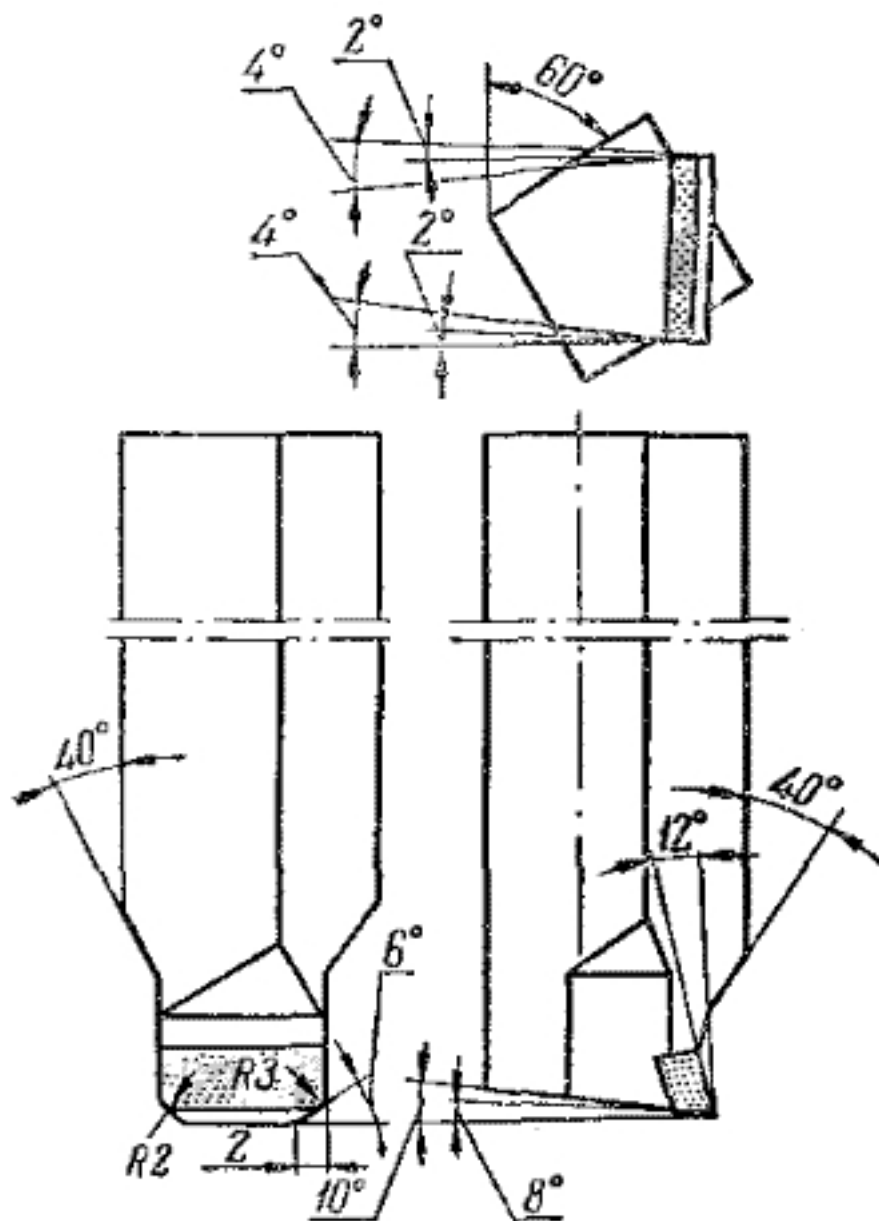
Широкий резец с повернутой режущей кромкой для чистового строгания.
